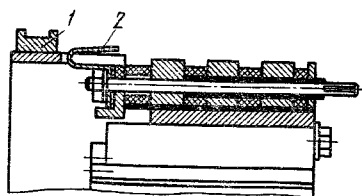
Короткозамыкающее приспособление с пружинными контактами
